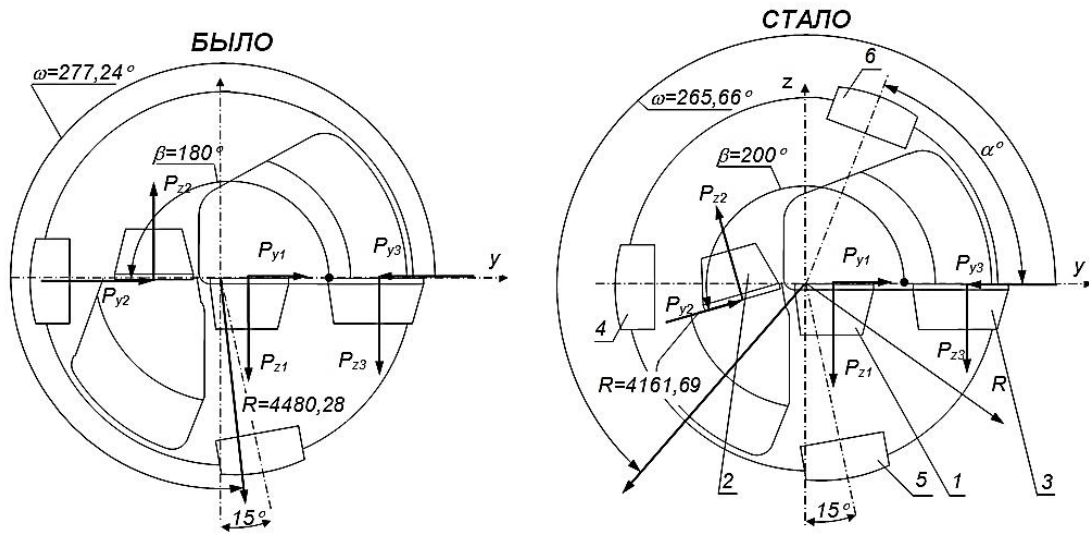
Схема новой конструкции инструмента для глубокого сверления отверстий
